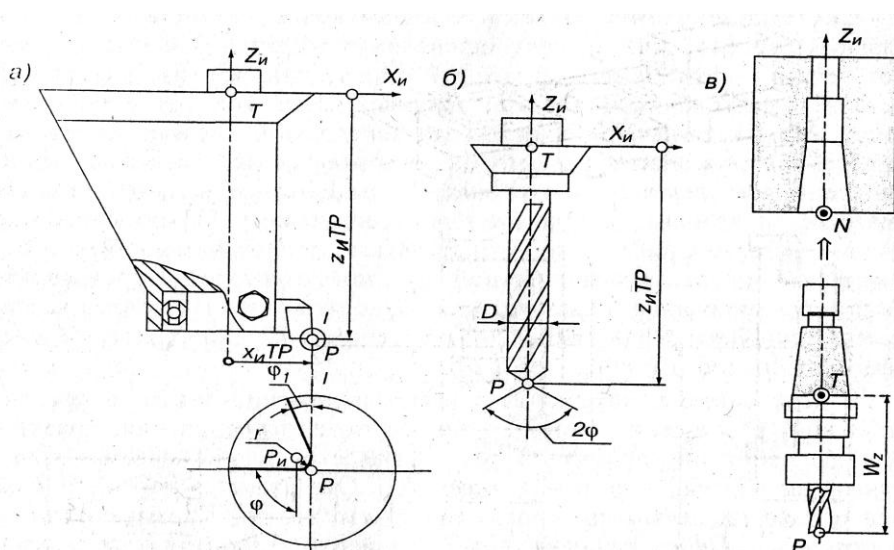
Система координат инструмента: а) резец; б) сверло; в) схема базирования инструмента
